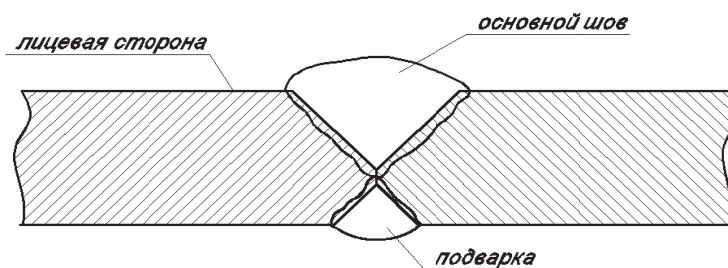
Сварной шов с несимметрично подготовленными кромками
